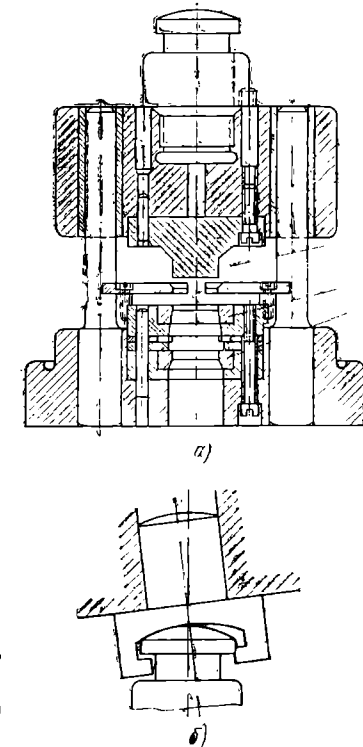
Зачистной штамп (а) и схема устройства плавающего хвостовика (б)
